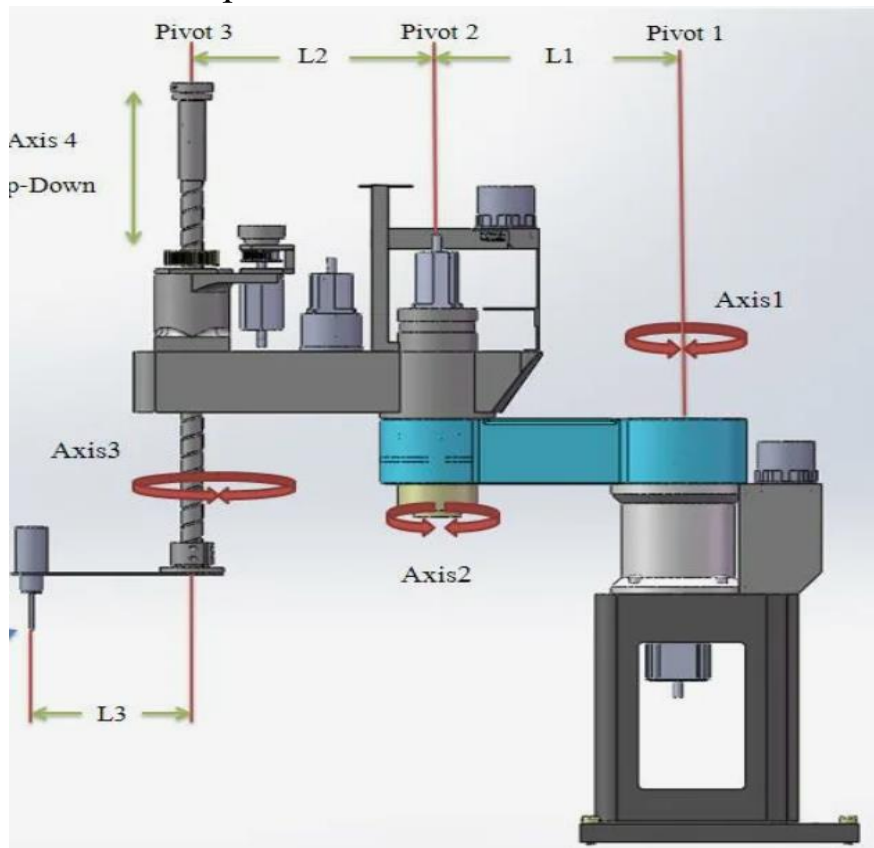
Схема движений руки манипулятора робота SKARA
